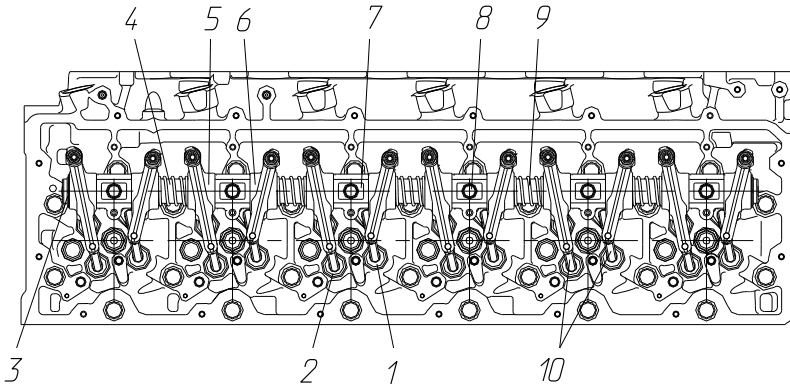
Вид сверху на механизм газораспределения, установленный в головке цилиндров:
